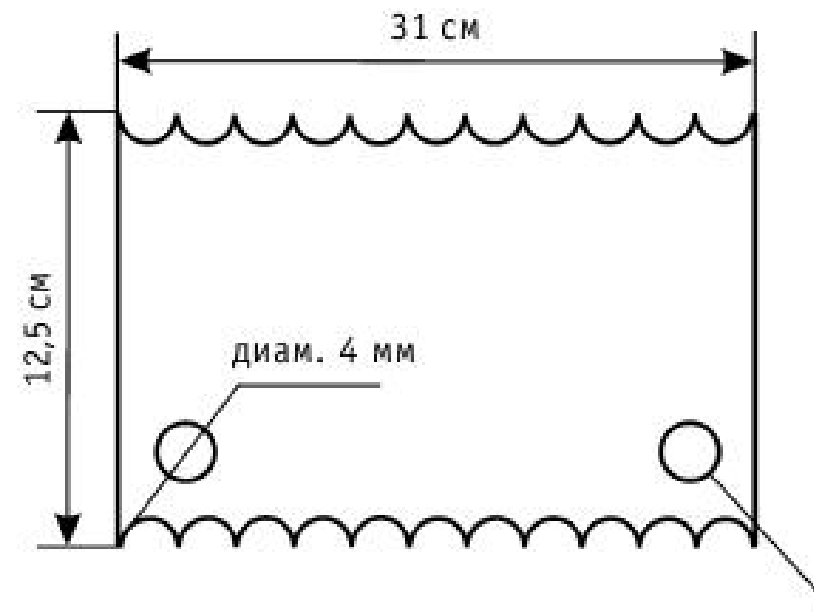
Внешний вид пластины для намотки нихромовой проволоки нагревателя
